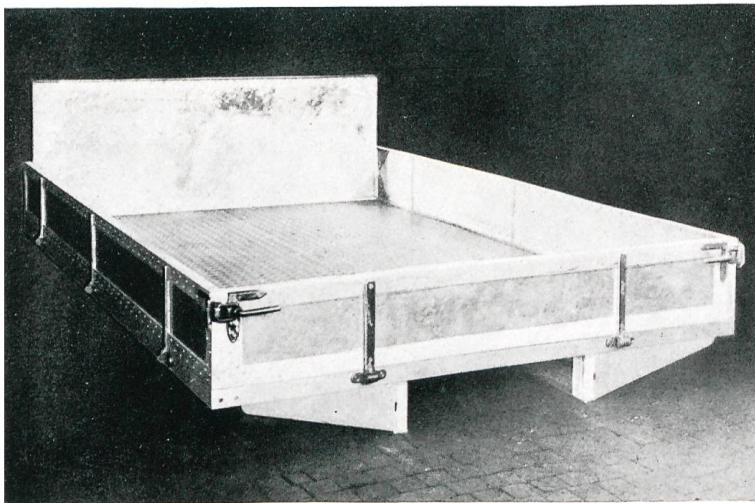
Leichtmetallbrücke mit Anticorodal-Warzenblech
